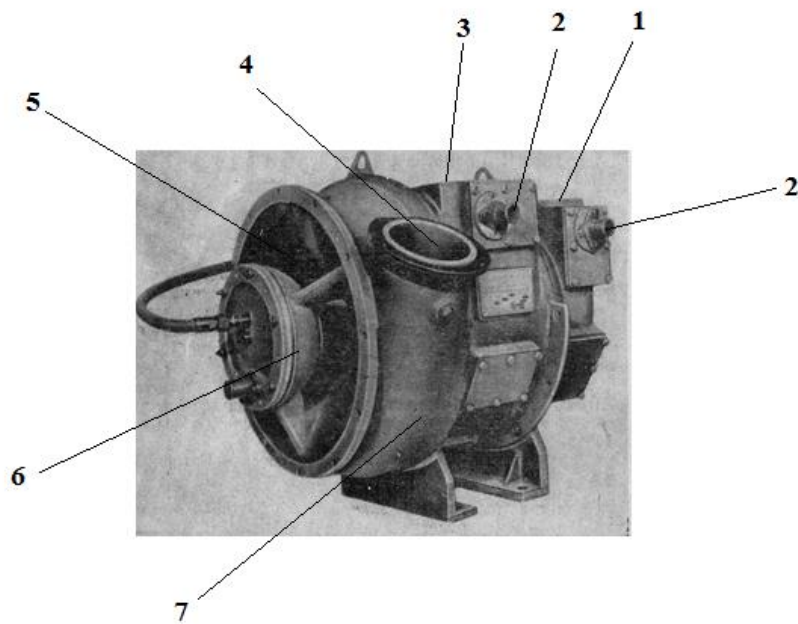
Загальний вид турбокомпресора: 1 – отвір для підведення газів; 2 – отвори для відведення охолоджуючої води; 3 – отвір для відведення газів; 4 – отвір з завитки для подачі повітря до ресивера; 5 – всмоктуючий отвір компресора; 6 – корпус упорно-опорного підшипника
